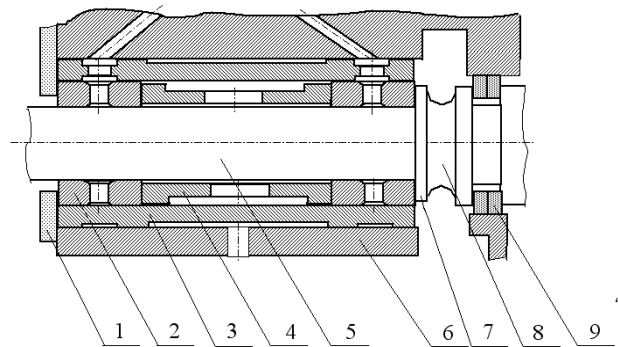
Конструкция подшипника с автономными пакетами ПВ и ПН втулок:
